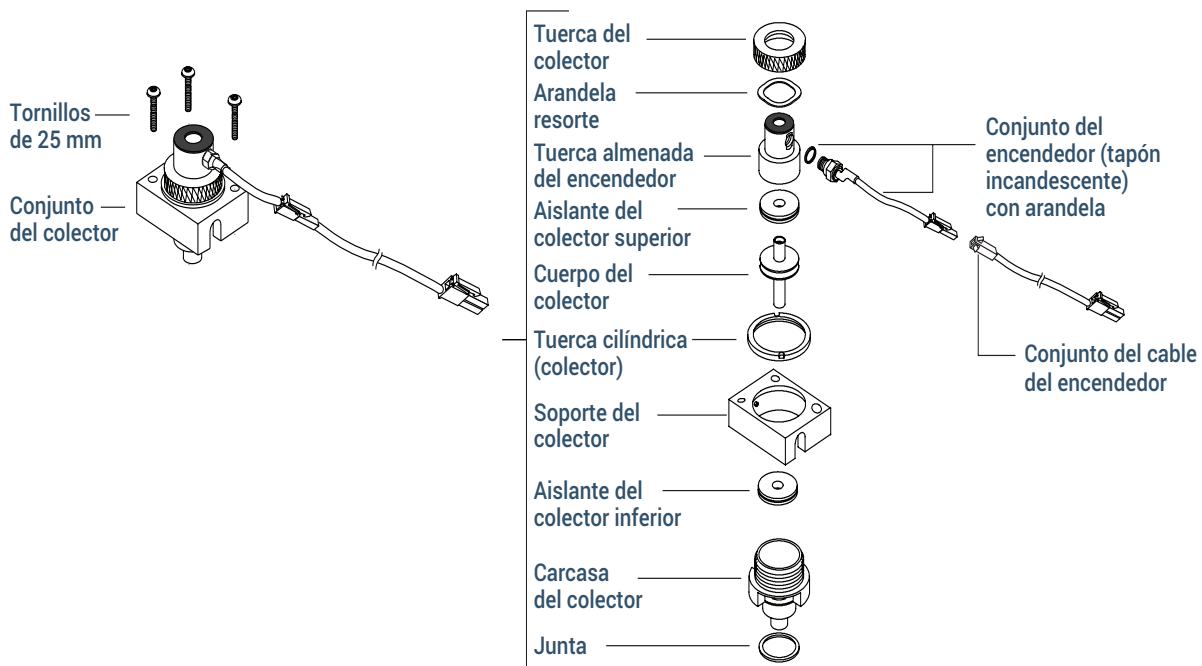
Vista detallada de piezas del conjunto del colector del FID
